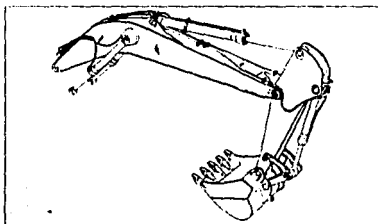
PLUMA Y BRAZO DE EXCAVADORA.
